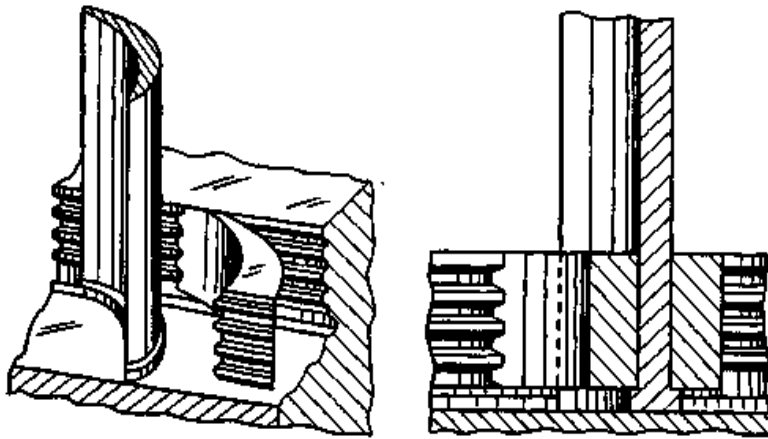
Реактивные лопатки из катаной профильной полосы
